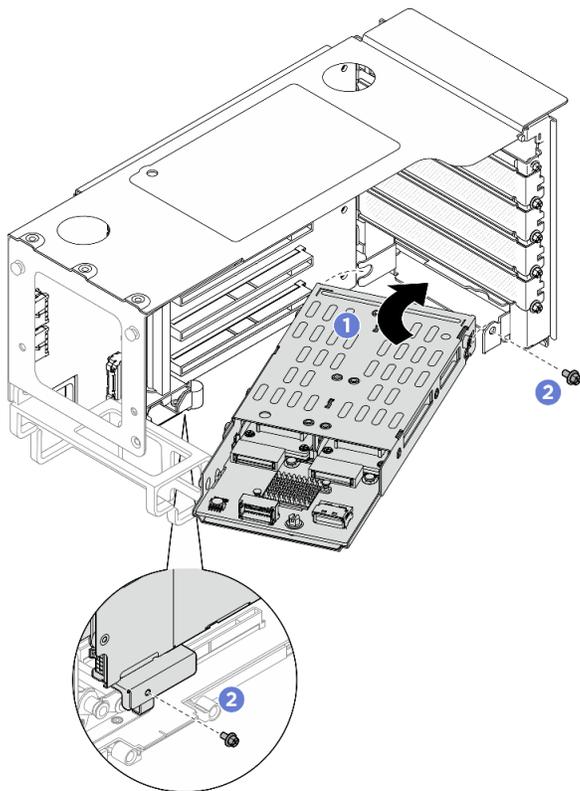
Installation du boîtier d'unités M.2 sur la carte mezzanine
